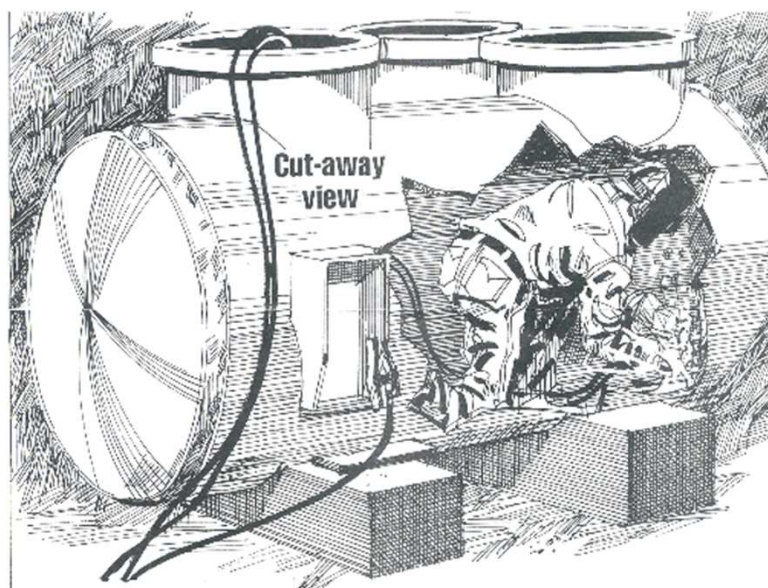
Reparações por soldadura. Fonte: gwpsafety.com
